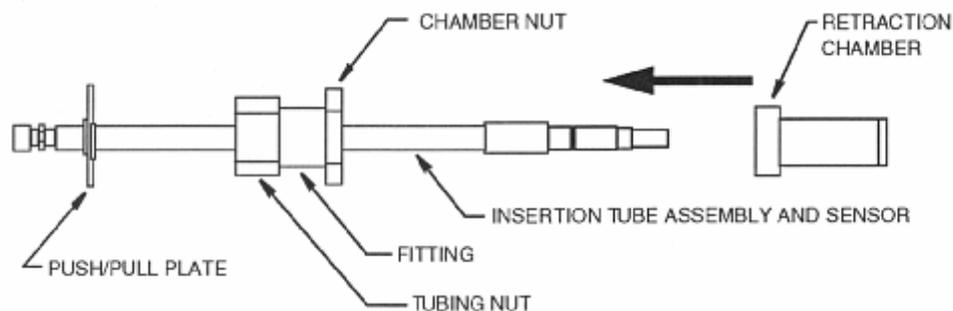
Retirada del conjunto del tubo de inserción del proceso
